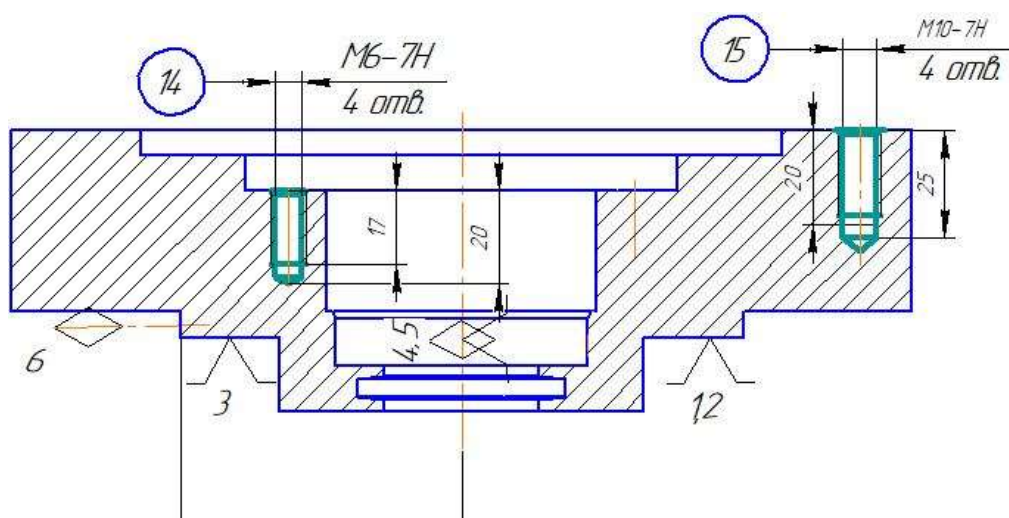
Ескіз механічної обробки із схемою базування (операція 015)
